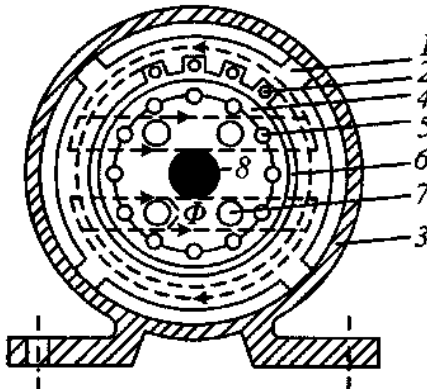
Конструктивна схема асинхронного трифазного двигуна: 1 – осердя статора, набране із листів електротехнічної сталі; 2 – трифазна обмотка статора; 3 – корпус (станина) статора; 4 – осердя ротора, теж набране з листів електротехнічної сталі; 5 – обмотка ротора; 6 – повітряний проміжок між ротором і статором; 7 – вентиляційні канали; 8 – вал машини
